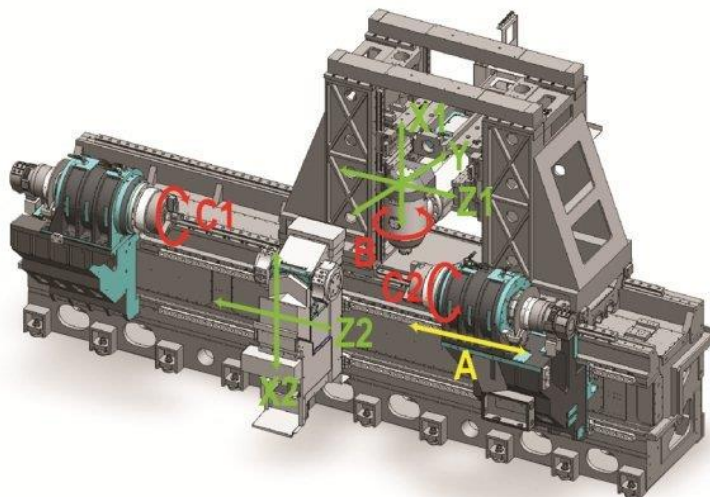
Координаты станка Takisawa TMT 4500 TT
